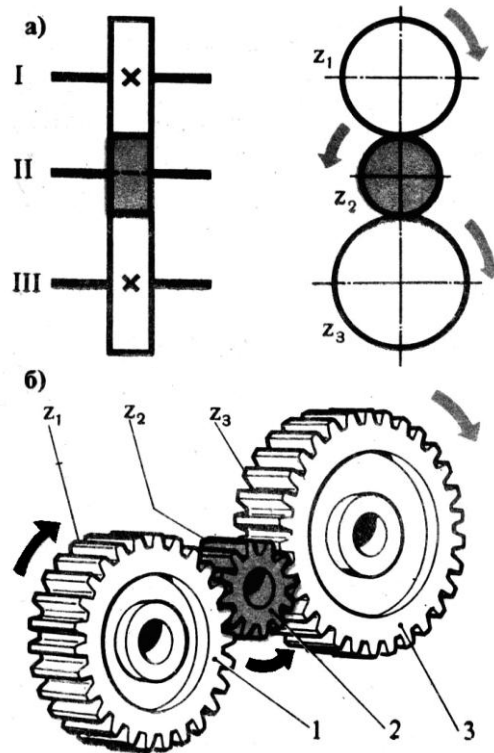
Передача з проміжним зубчастим колесом:
